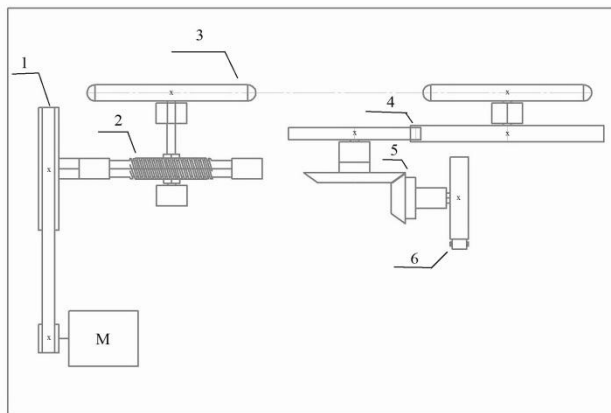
Передаточный механизм: 1) ременной привод, 2) червячный привод, 3) цепной привод, 4) цилиндрический привод, 5) конический привод, 6) фрикционный привод
